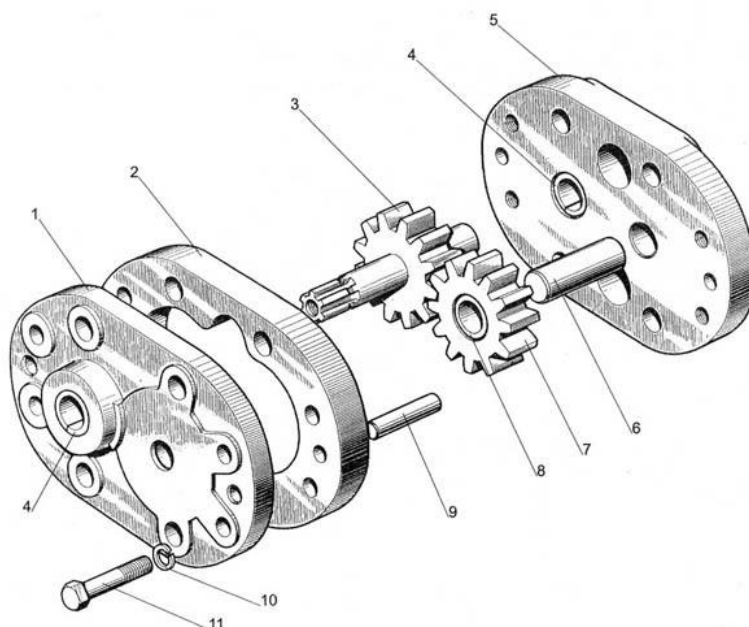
Конструкция шестеренного насоса с внешним зацеплением шестерен
